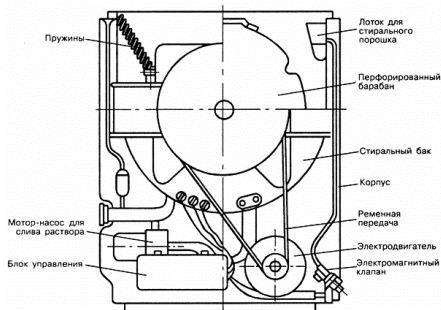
Внешний вид и устройство стиральной машины КИ-ШИНЭУ-4.
